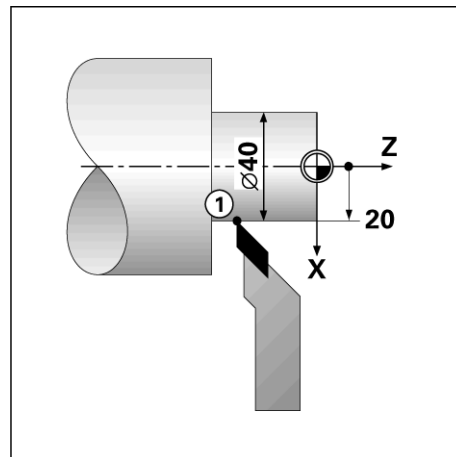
Werkstück zum Beispiel „Radius-/ Durchmesser-Anzeige“
